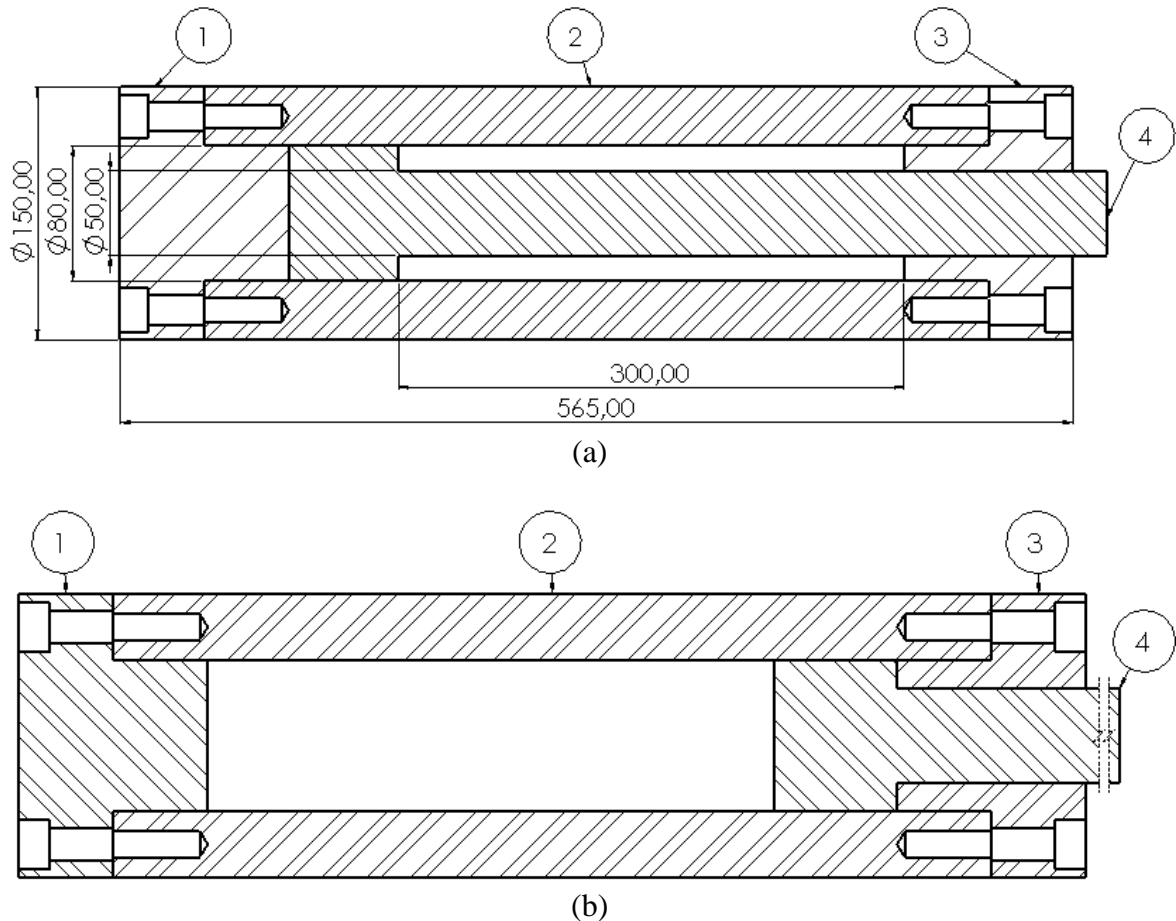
(a) Vista de seção, com as dimensões principais atuador hidráulico na posição recuada. (b) Vista de seção, atuador hidráulico na posição avançada. (1) Flange inferior, (2) Casco, (3) Flange superior, (4) Êmbolo. Dimensões em mm.
